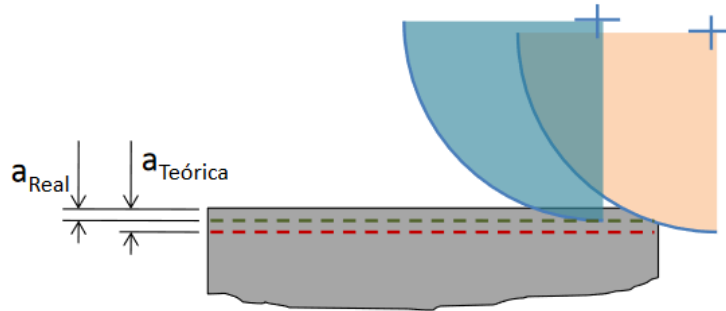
Profundidad de pasada real vs teórica. Fuente: Escuela Técnica Superior de Ingeniería
